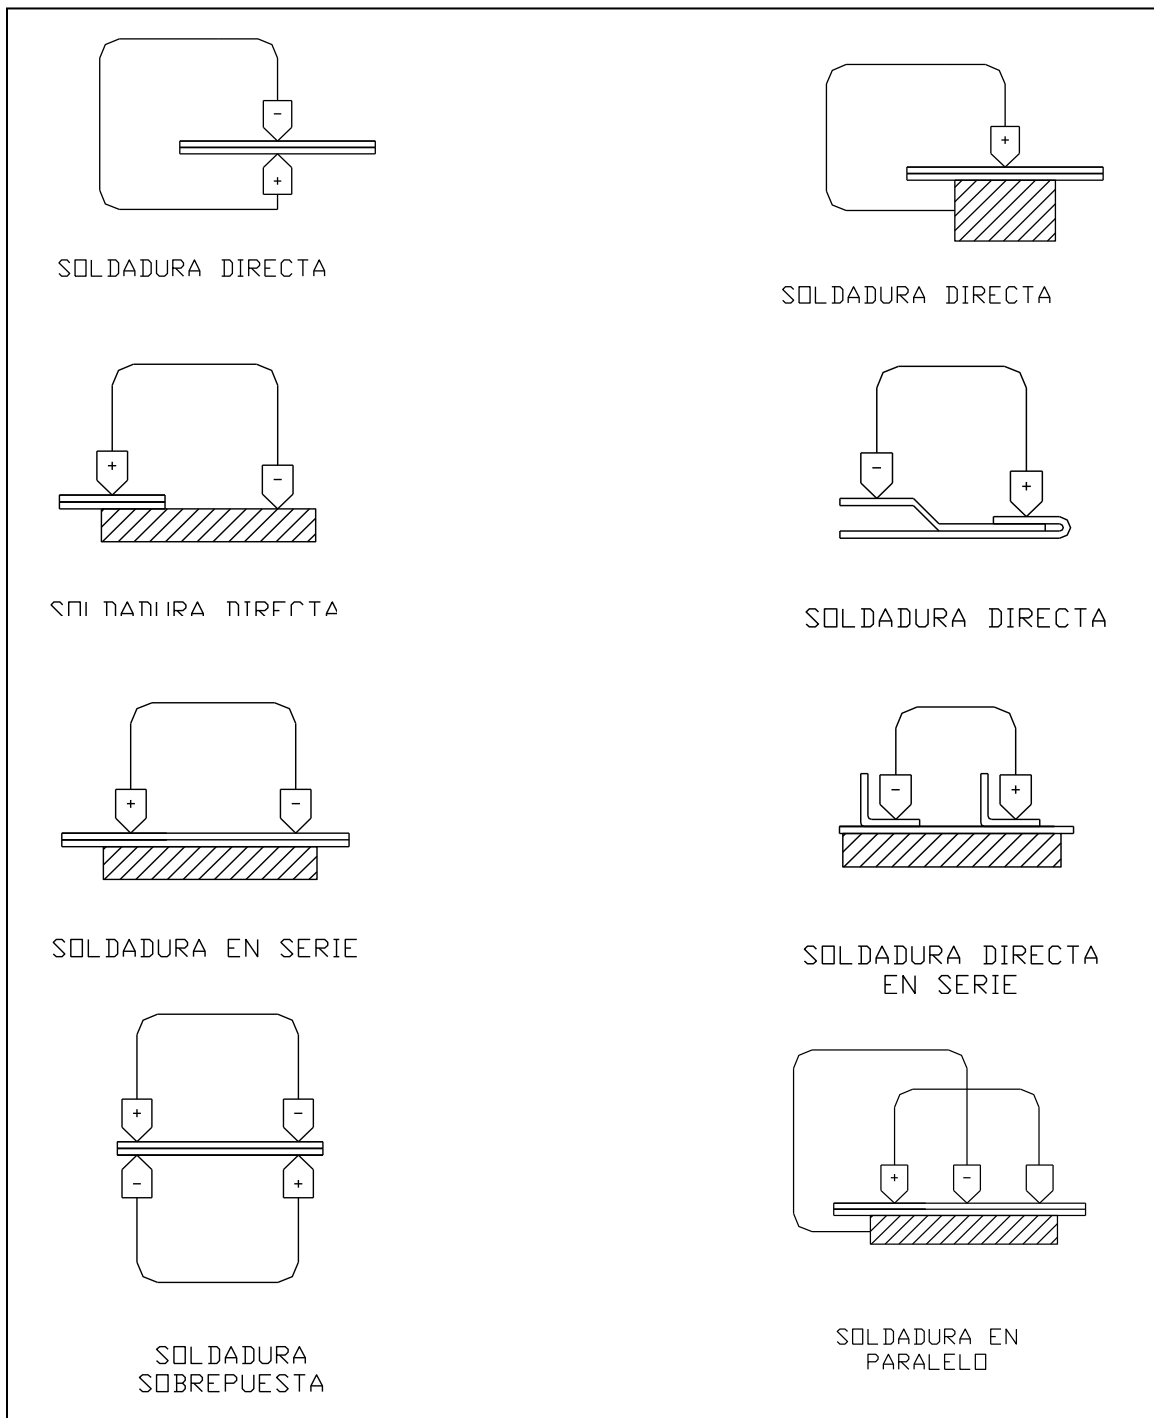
Tipos de aplicación de soldadura de resistencia.
